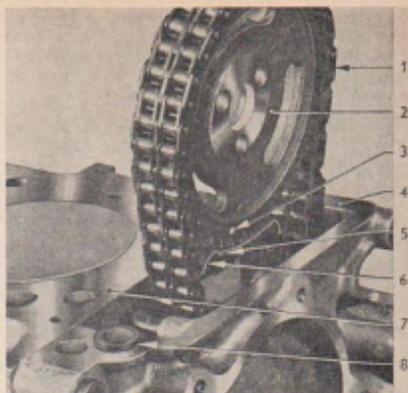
Gummidichting für Wasserführung in Ausenkung des Steuergehäuses
